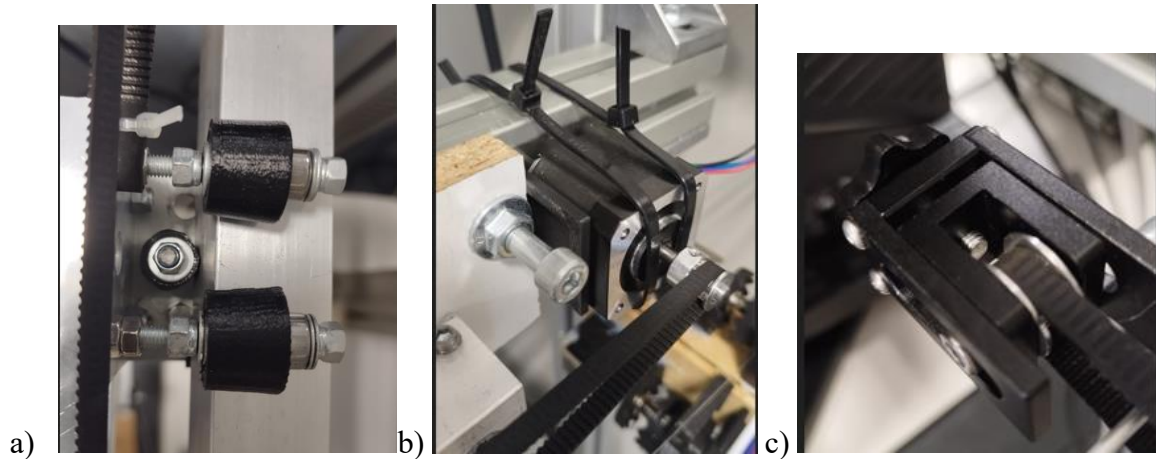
Correa GT2 abierta unida a los distintos elementos: a) Al carro portador, b) Engranada con el acople GT2 del motor, c) Engranada con la polea dentada del soporte auxiliar.
